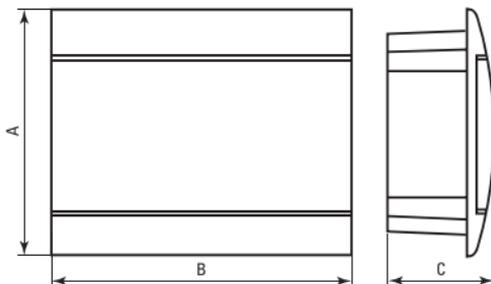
Габаритные размеры щитов ЩРВ-П (пром. упаковка)
